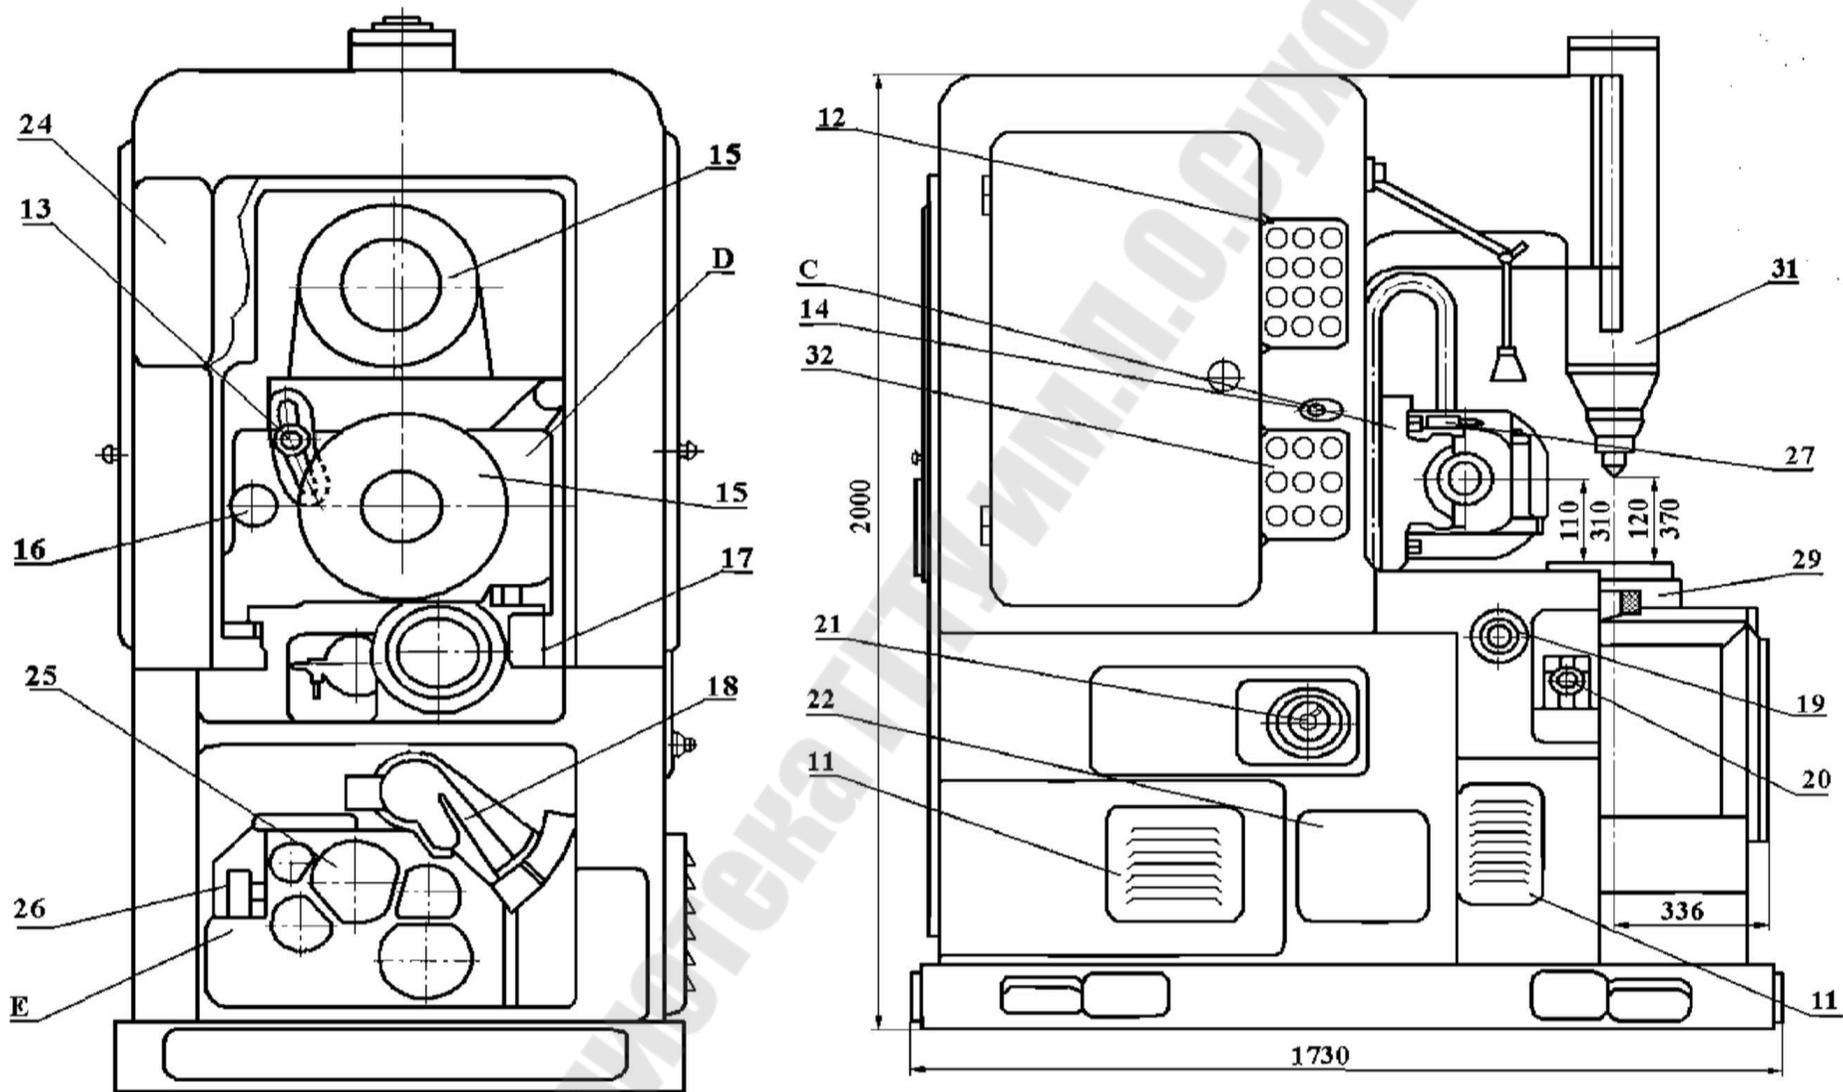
Общий вид зубофрезерного станка (вид сбоку и сзади)
